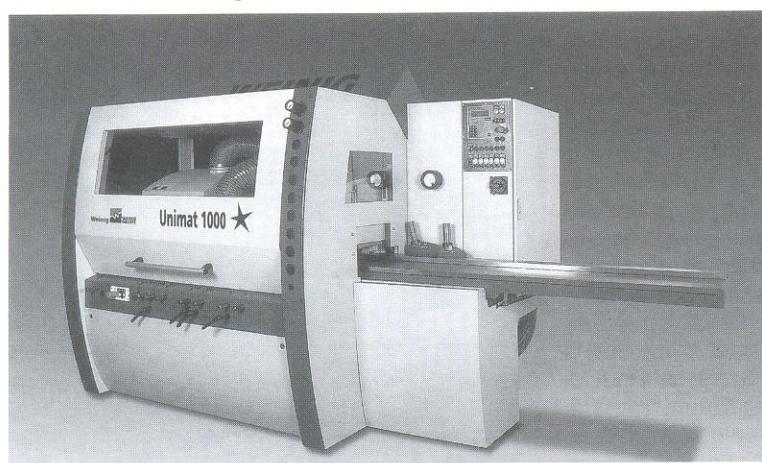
Четырёхсторонний продольно-фрезерный станок-полуавтомат Unimat 1000
